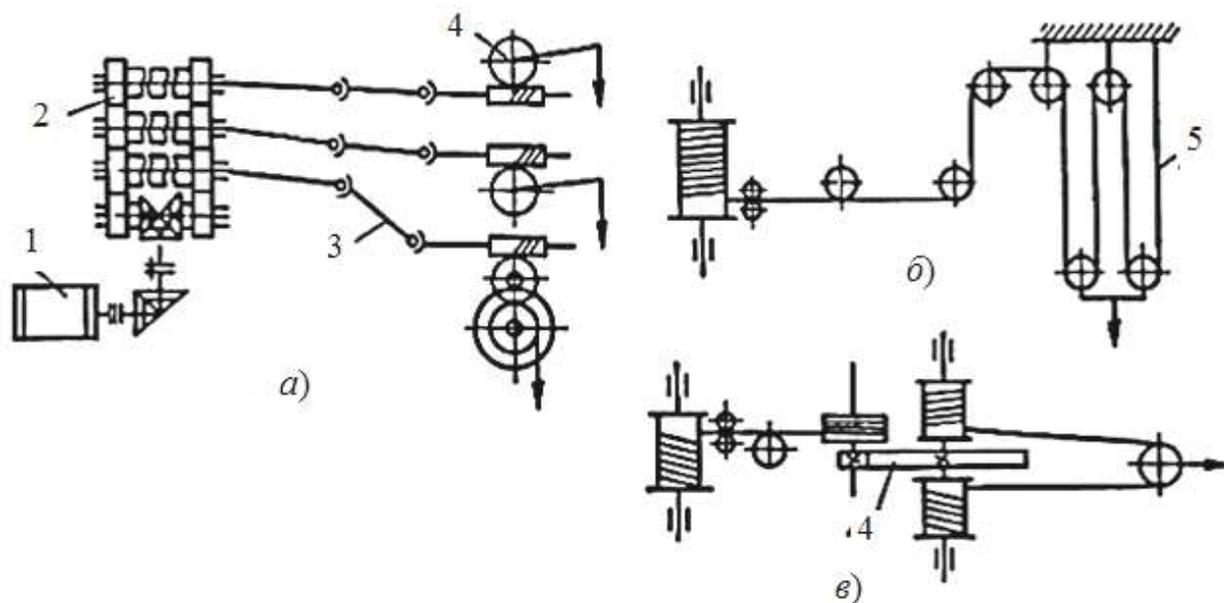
Схемы механических систем управления: а – редукторная; б – канатно-блочная с полиспастом; в – канатно-блочная с зубчатой передачей; 1 – двигатель; 2 – механизм реверса; 3 – карданный вал; 4 – редуктор; 5 – полиспаст.
